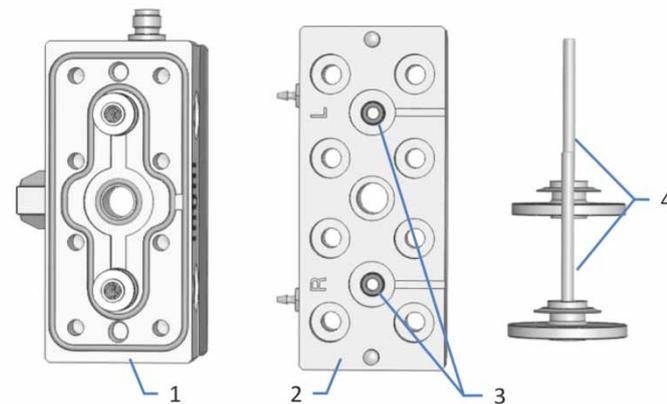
Pumpenkopf, Hinterspülplatte und Kolben entfernt
